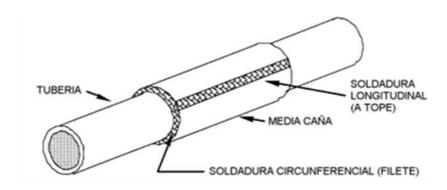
Camisa de refuerzo (envolvente circunferencial completa soldada)
